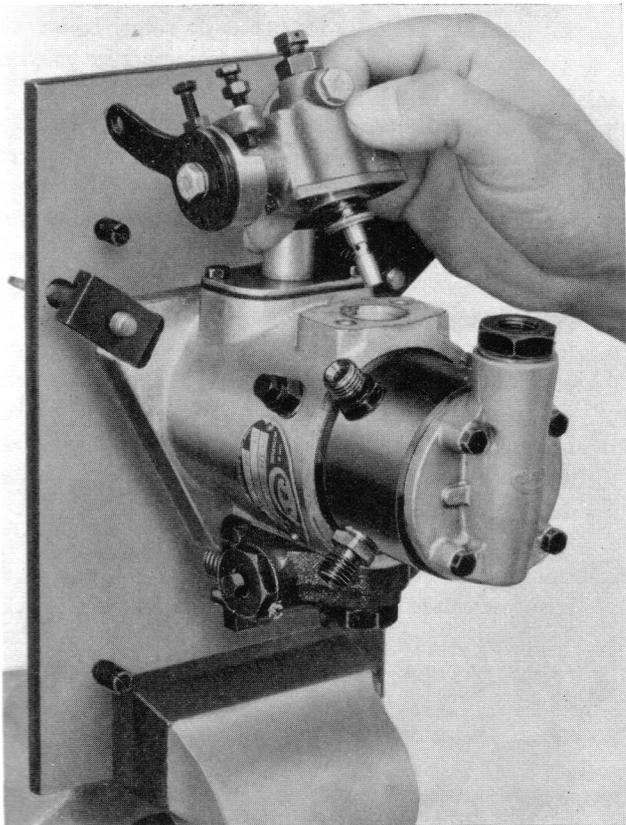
Dépose d'un régulateur hydraulique à montage réversible
